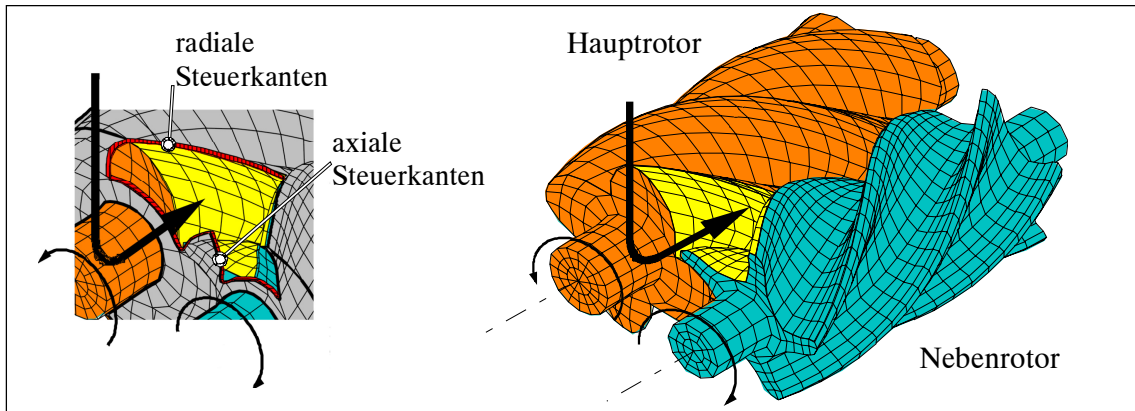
Arbeitsspiel des konventionellen Schraubenmotors – Füllung der Arbeitskammer durch Steuerflächen im Gehäuse
